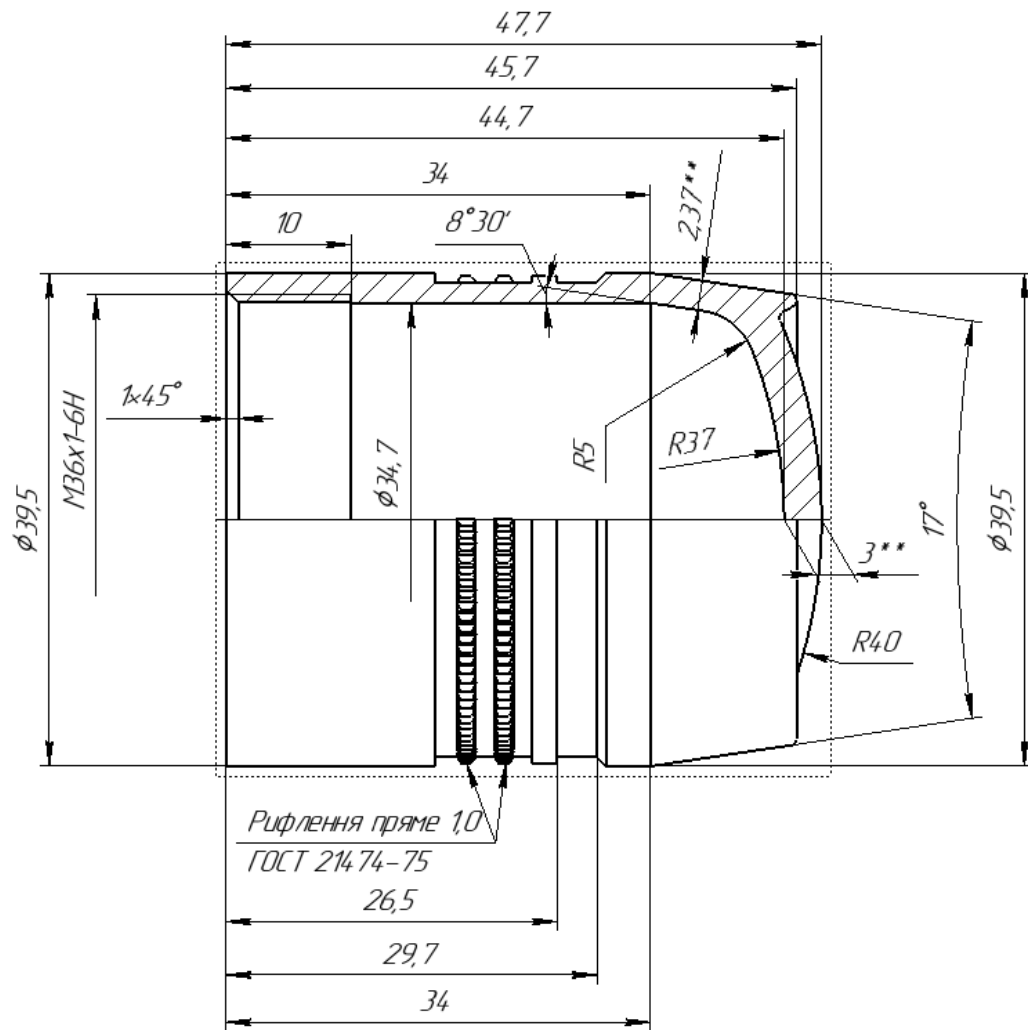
Ескіз корпусу гранатометного пострілу, що виготовляється за допомогою механічної обробки
